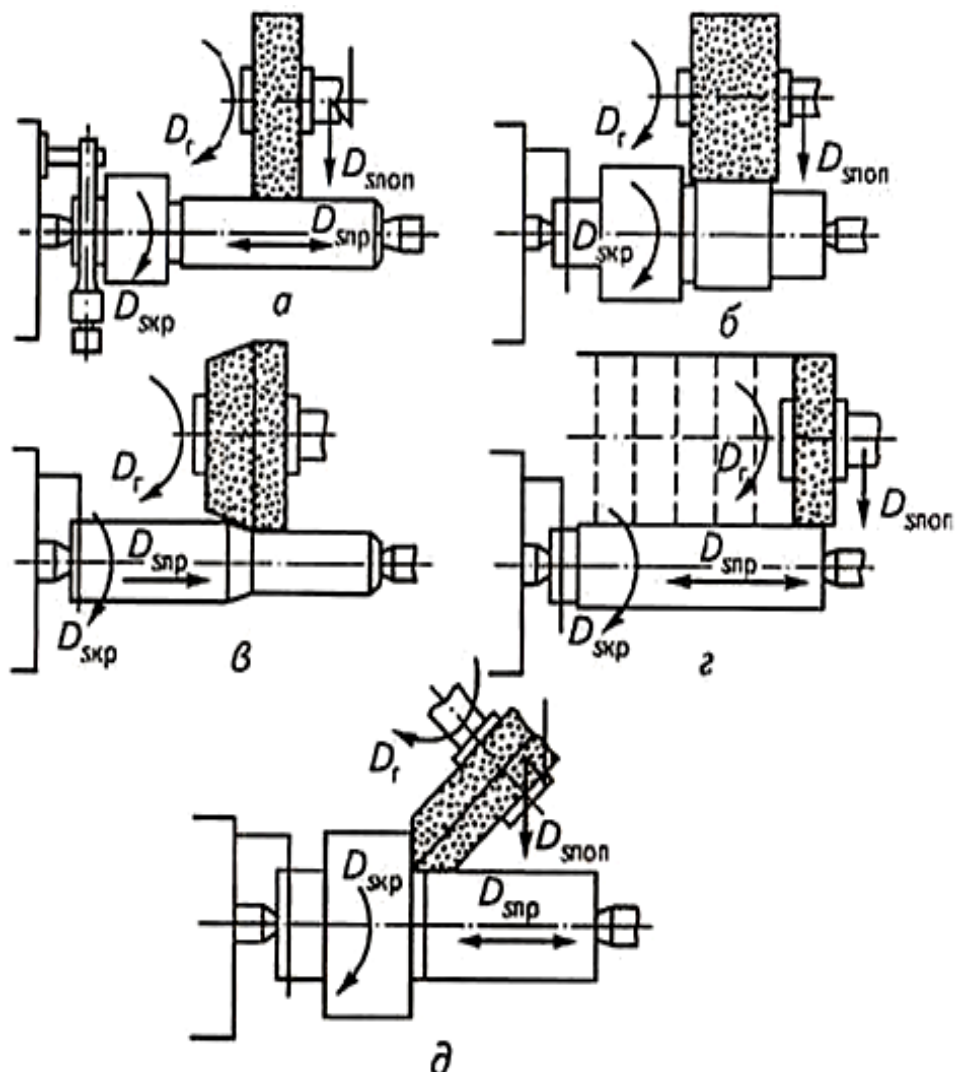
Схемы обработок заготовок на круглошлифовальных станках
